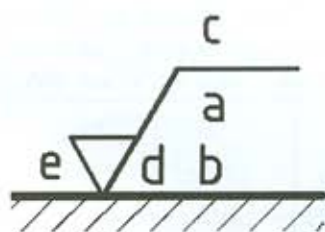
Základní značka struktury povrchu (rozměry platí pro výšku písma 3,5 mm)
